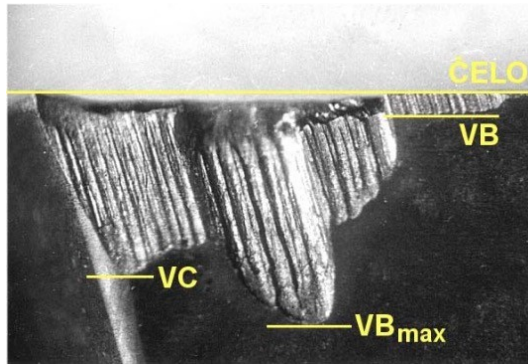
Nízká hodnota VB kombinovaná s vysokou hodnotou VB_{max} [6]
